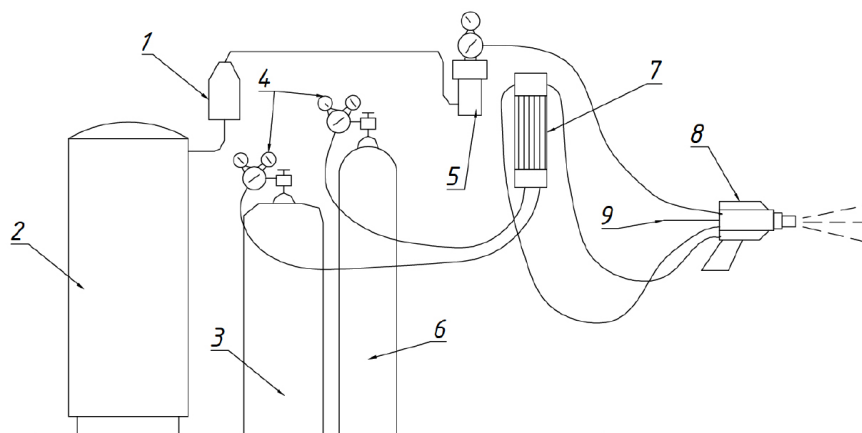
Схема оборудования поста для напыления расплавленного металла, подаваемого в горелку в виде проволоки: 1 – осушитель воздуха; 2 – ресивер со сжатым воздухом; 3 – баллон с горючим газом; 4 – редукторы; 5 – фильтр; 6 – баллон с кислородом; 7 – ротаметры; 8 – напылительная горелка; 9 – канал для подачи проволоки
